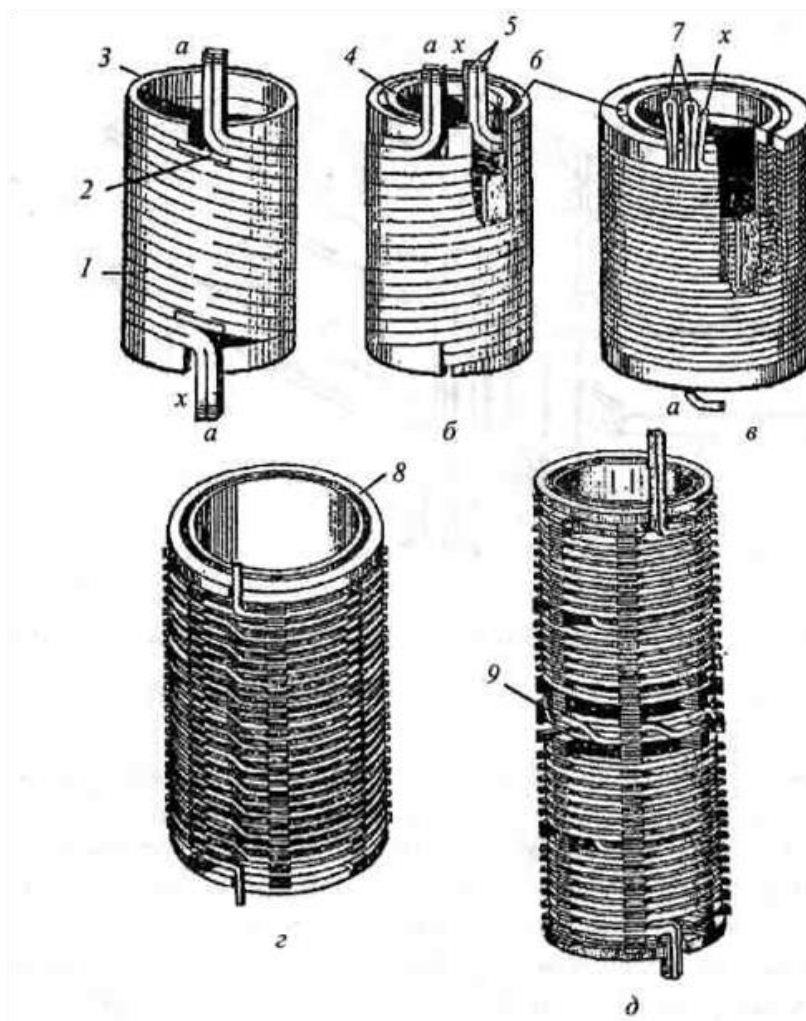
Циліндричні обмотки силових трансформаторів: а - одношарова; б - двошарова; в - багатошарова; г - безперервна; д - гвинтова; 1 - витки з прямокутного провода; 2 - електрокартонна коробка для підсилення ізоляції крайніх витків обмотки; 3 - резервні вирівнюючі кільця, 4 - паперово-бакелітовий циліндр; 5 - кінець першого шару обмотки, 6 - вертикальні рейки; 7 - внутрішні відгалуження обмотки; 8 - опорне ізоляційні кільце; 9 - транспозиція витків обмотки [1]
